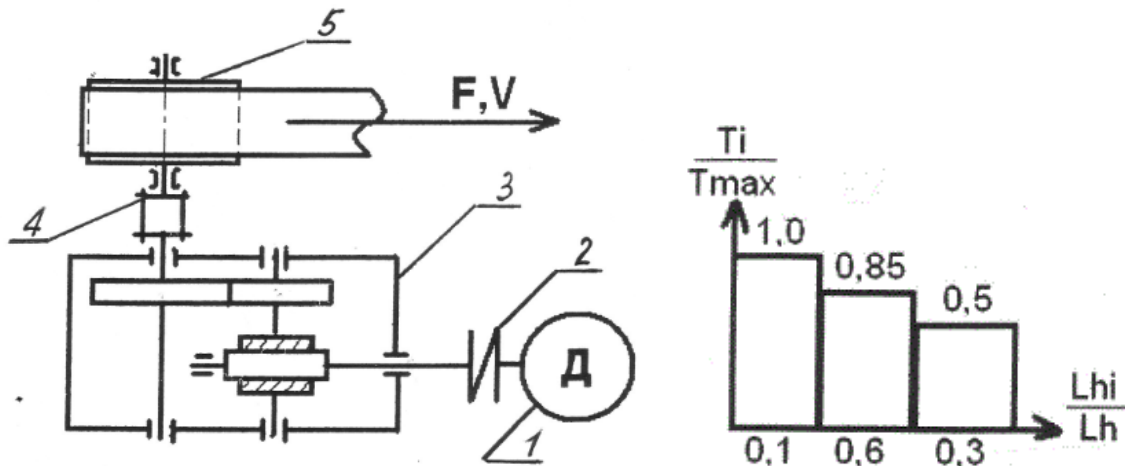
Схема двухступенчатого червячно-цилиндрического редуктора
